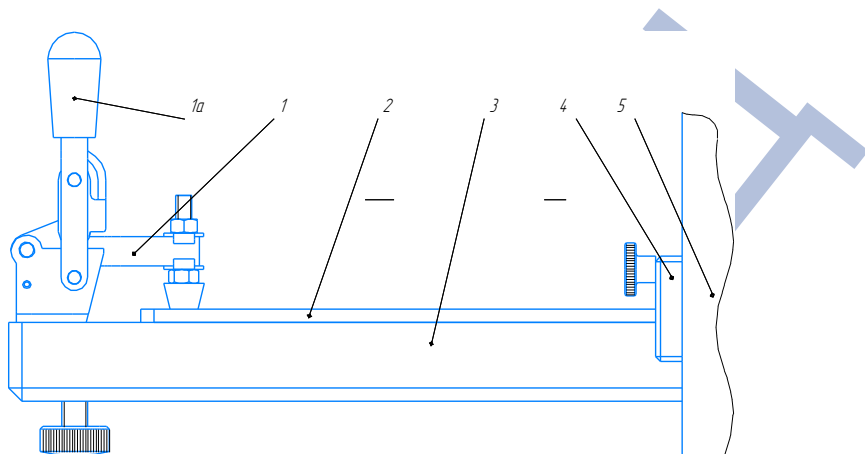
Система фиксации образца (1 – эксцентриковый прижим; 1а – рукоятка эксцентрикового прижима; 2 – прижимная планка; 3 – основание прибора; 4 – механизм регулировки прижима для разной толщины образца; 4- корпус)
